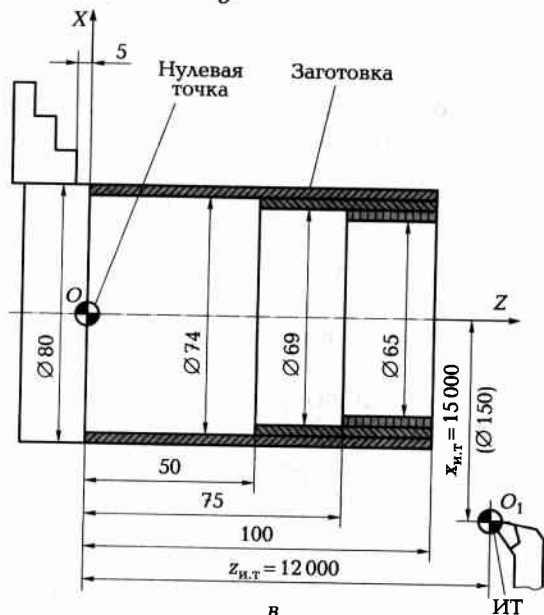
Схема наладки токарного станка мод. 16К20Т1 на обработку ступенчатого вала:
